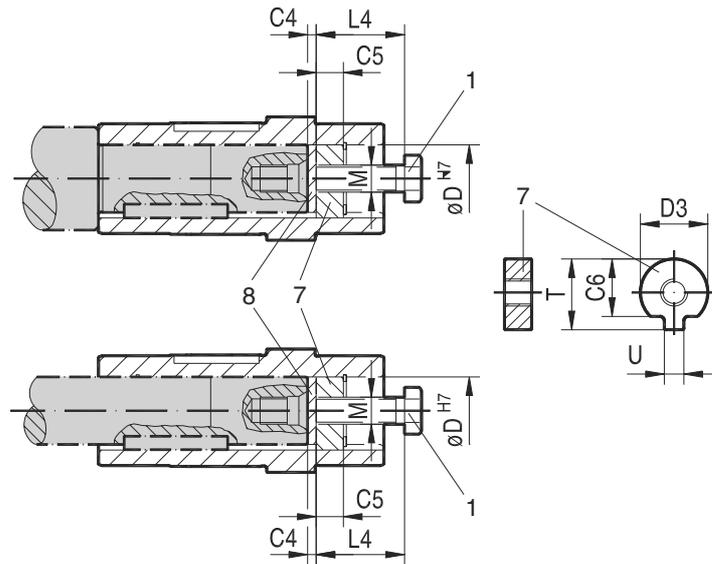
Kit de montaje y desmontaje SEW-EURODRIVE
